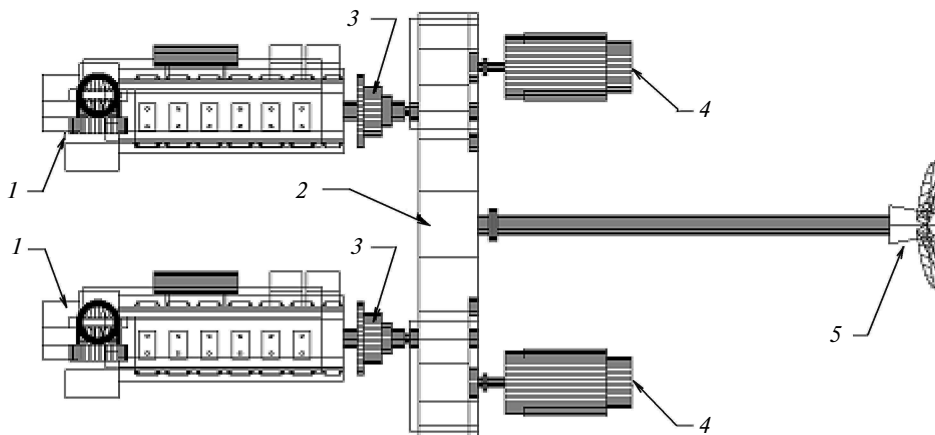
Двухмашинный дизель-редукторный агрегат с отборами мощности (1 — дизель; 2 — суммирующий редуктор; 3 — соединительно-разобщительная муфта; 4 — валогенератор; 5 — винт регулируемого шага)
